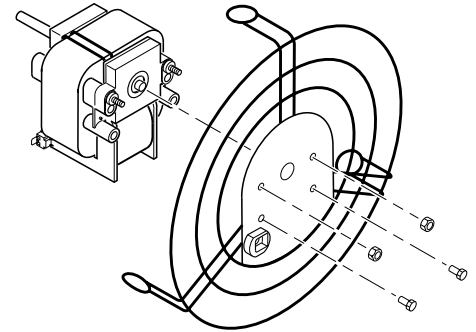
Retrait ou fixation de la grille de ventilateur sur le moteur
